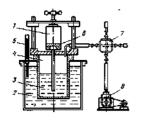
Схема установки для литья термопластичных шликеров: 1 - форма; 2 - термостат; 3 - шликер; 4 - бачок; 5 - контактный термометр; 6 - прижимное устройство; 7 - редуктор; 8 - вакуумный насос
